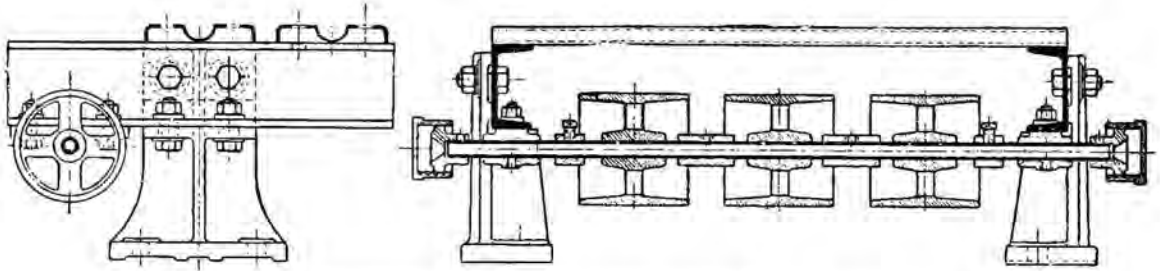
Самоустанавливающийся подшипник Webster с кольцевой смазкой для поддерживающих роликов.
